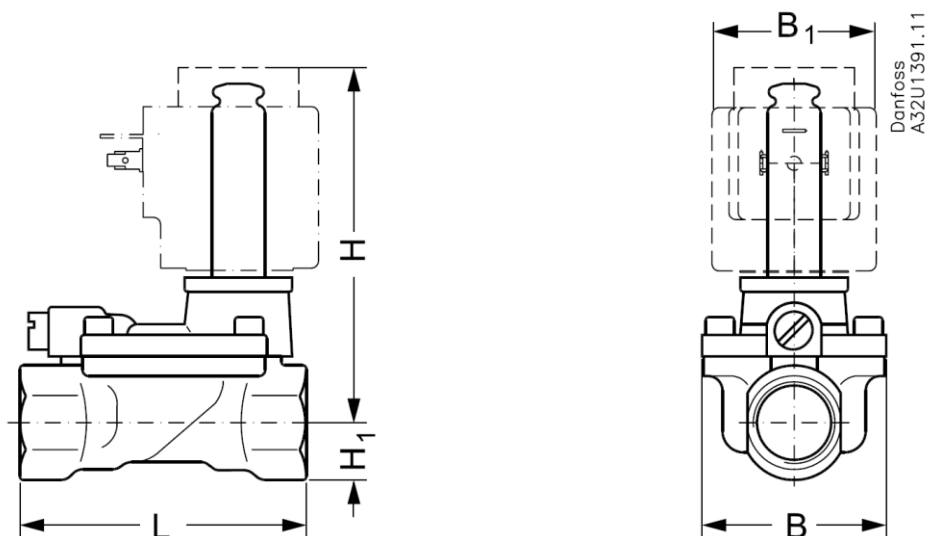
Габаритные и присоединительные размеры клапана типа EV220B
